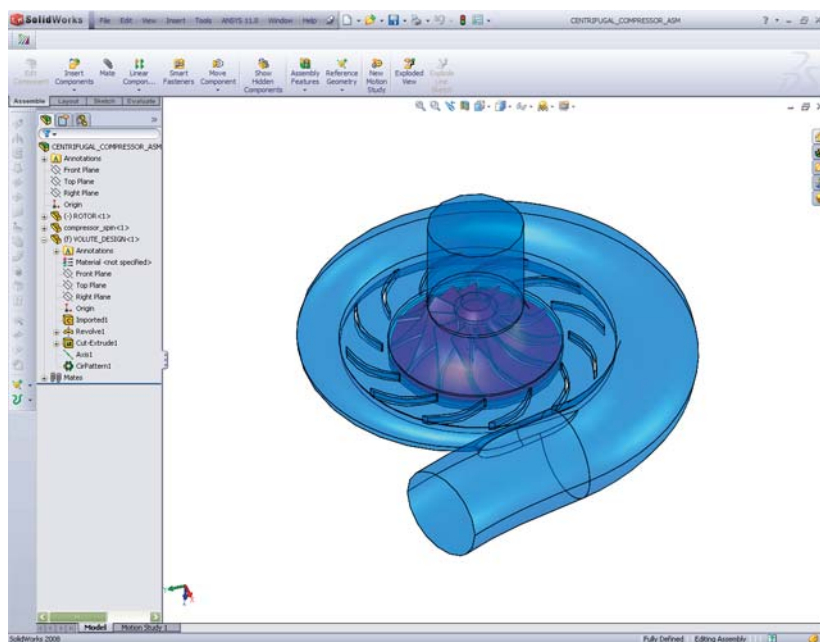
3D модель центробежного компрессора в SolidWorks
